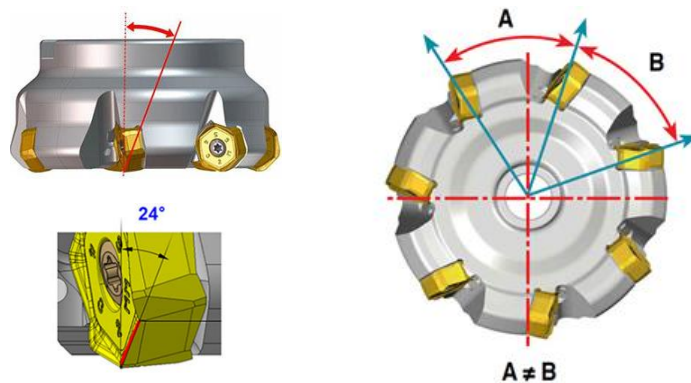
Торцева фреза CHASE12MILL компанії TaeguTec
